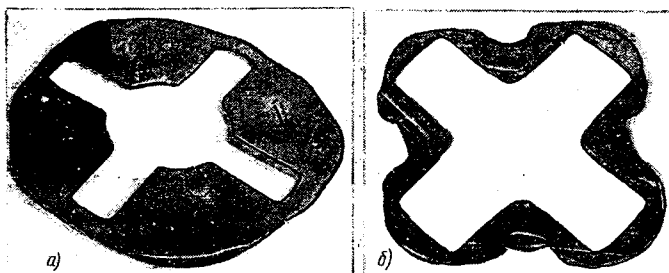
Изготовление заготовки в штампе открытого типа (а) и путем полузакрытого выдавливания (б)
